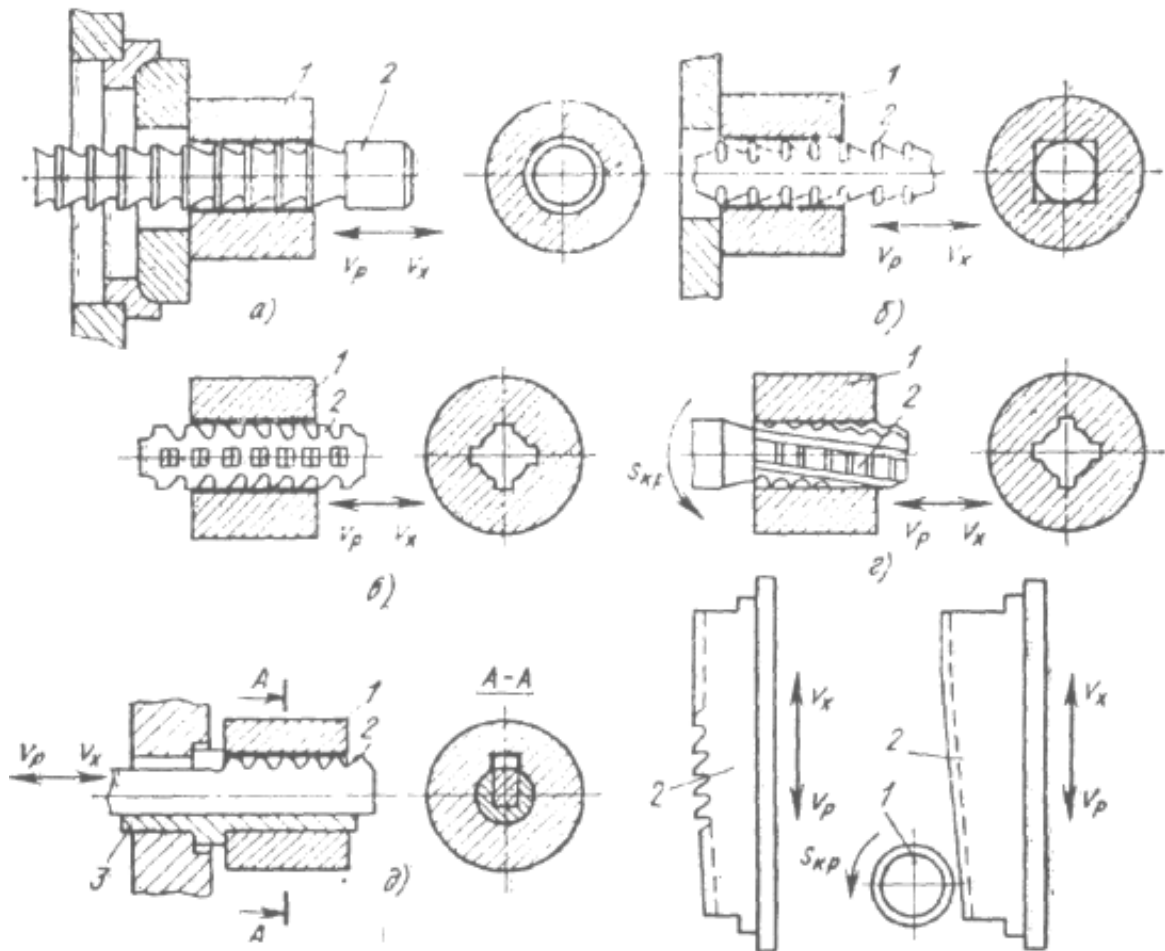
Обработка заготовок протяжками: а – круглой; б – квадратной; в, г – шлицевой; д – шпоночной
